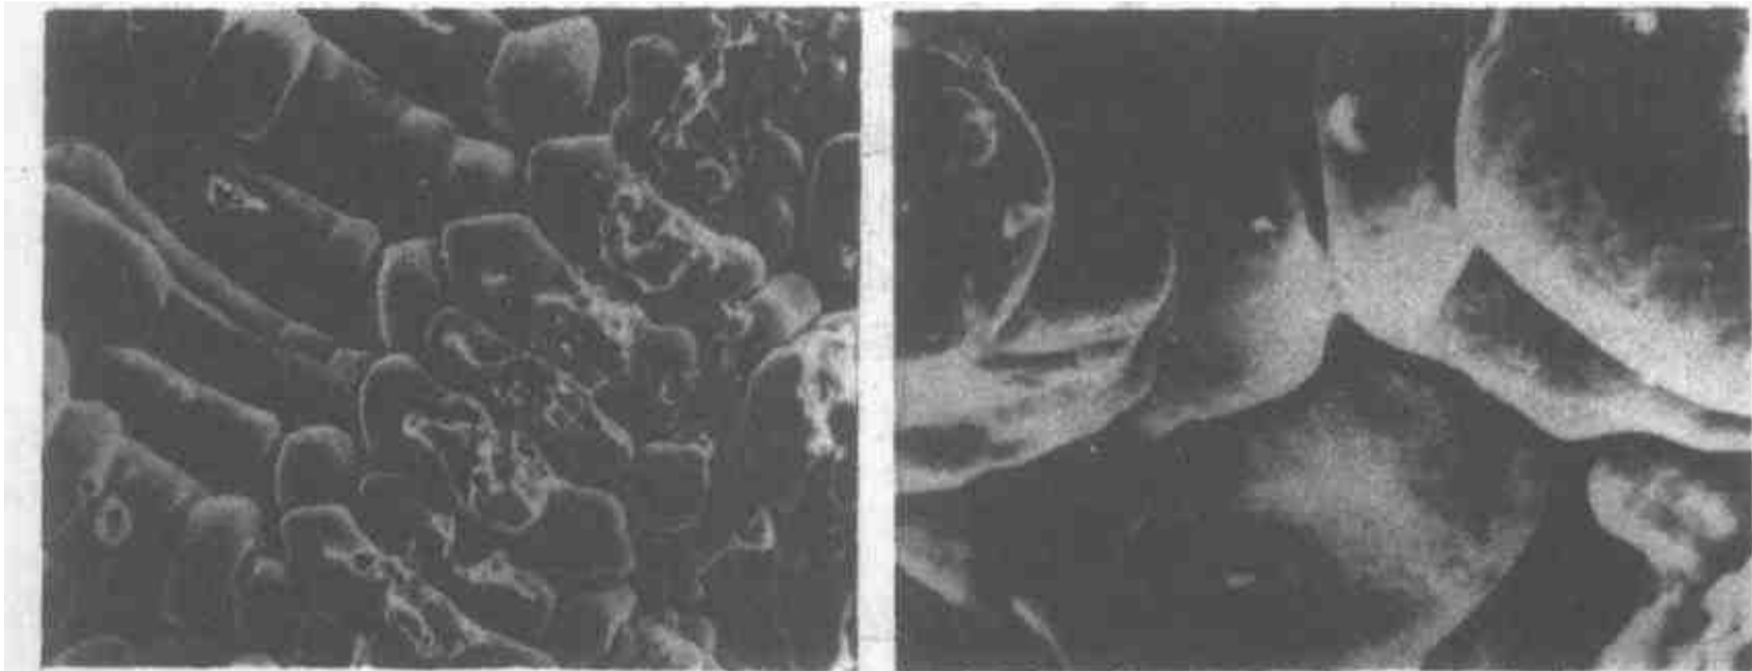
焊缝结晶裂纹断口形貌 1000×
